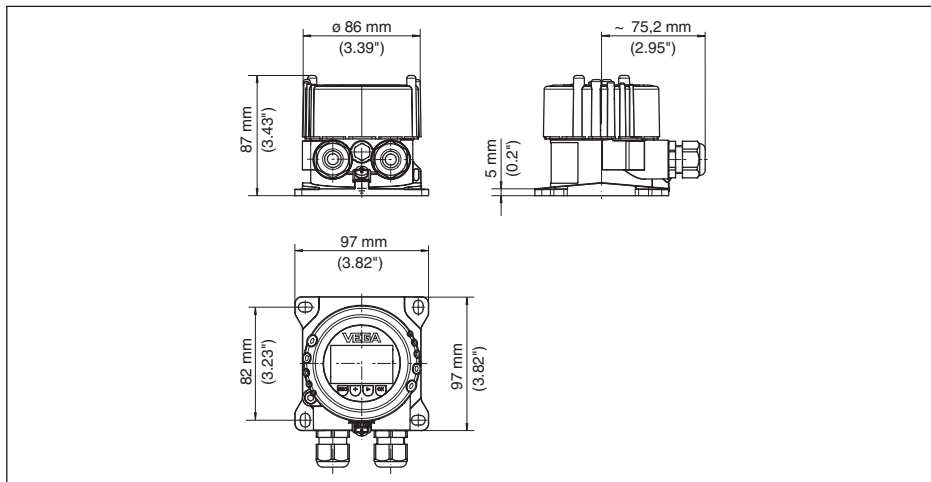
VEGADIS 82 с алюминиевым корпусом
